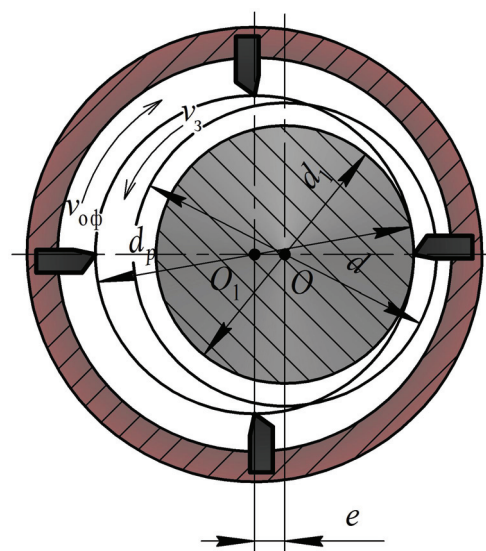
Схема нарезания резьбы охватывающей фрезой:
